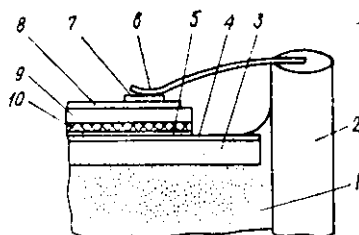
Полупроводниковая ИС (схематический разрез): 1 — ножка корпуса; 2 — позолоченный коваровый вывод корпуса; 3 — ковар; 4 — слой золота; 5 — сплав золото—германий; 6 — алюминиевая проволока; 7 — контактная площадка; 8 — пленка оксида кремния; 9 — кристалл кремния; 10 — сплав золото—кремний.
